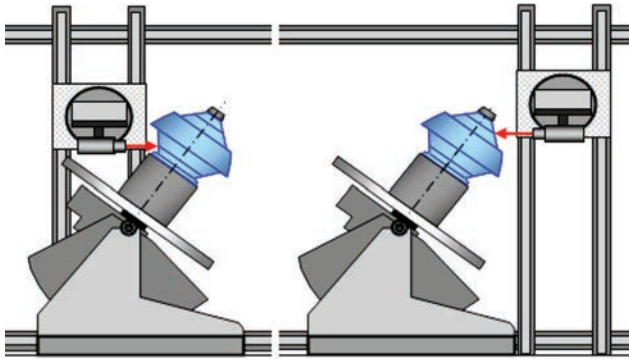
Пример схемы сварки вращающихся деталей сложной формы с помощью сварочного манипулятора с наклонной осью вращения
